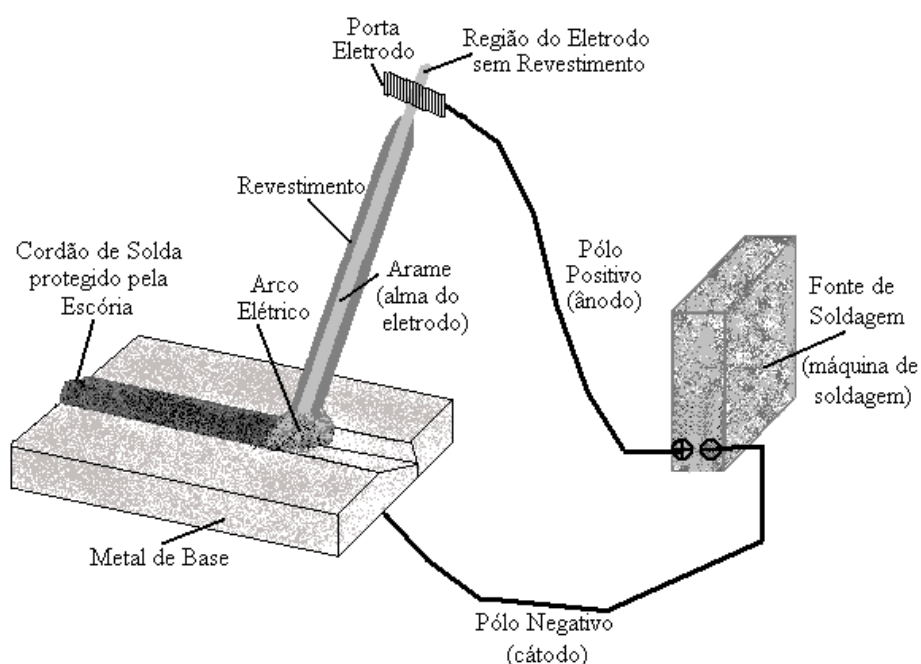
Equipamento para Soldagem com Eletrodo Revestido (Bracarense, 2014).
